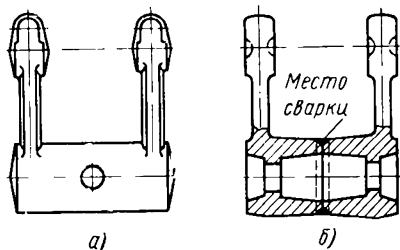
Два варианта поковки: *a* — цельная; *b* — сваренная из двух поковок
